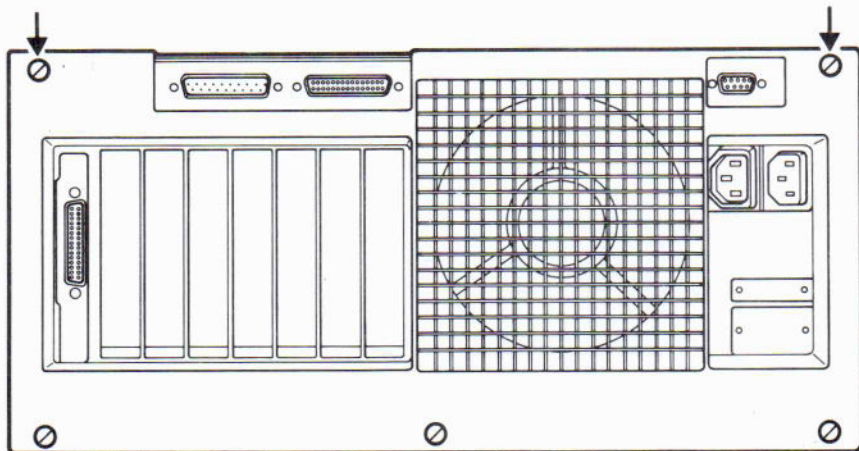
Schrauben zur Befestigung der Grundplatte
